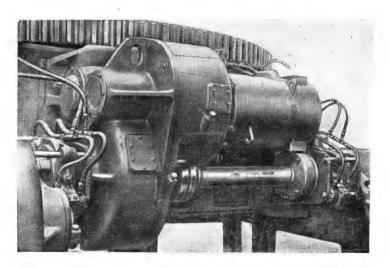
Общий вид ходового механизма экскаватора ЭКГ-4,6Б
